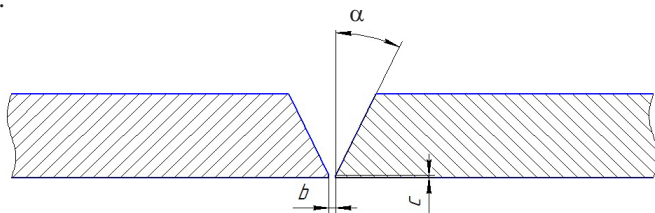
Параметры подготовки и сборки свариваемых пластин:
